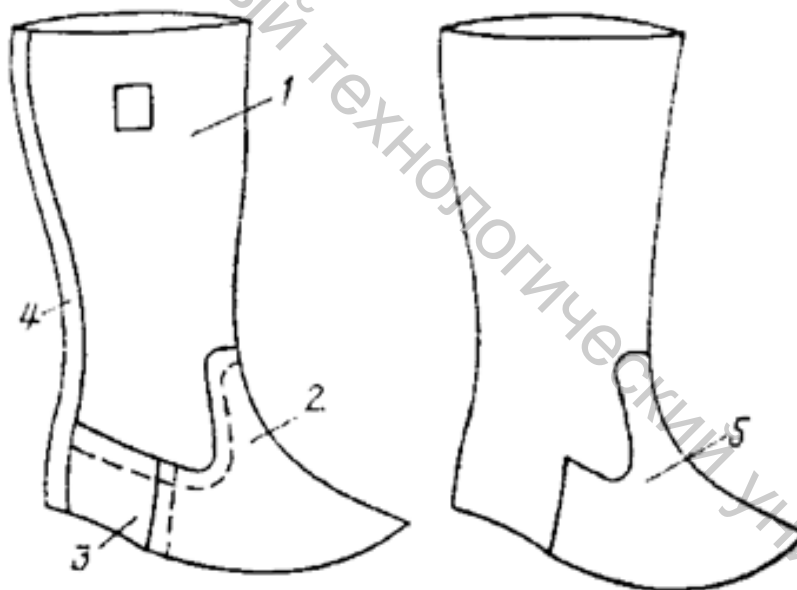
Детали верха сапог с голенищами из обувной кирзы:
